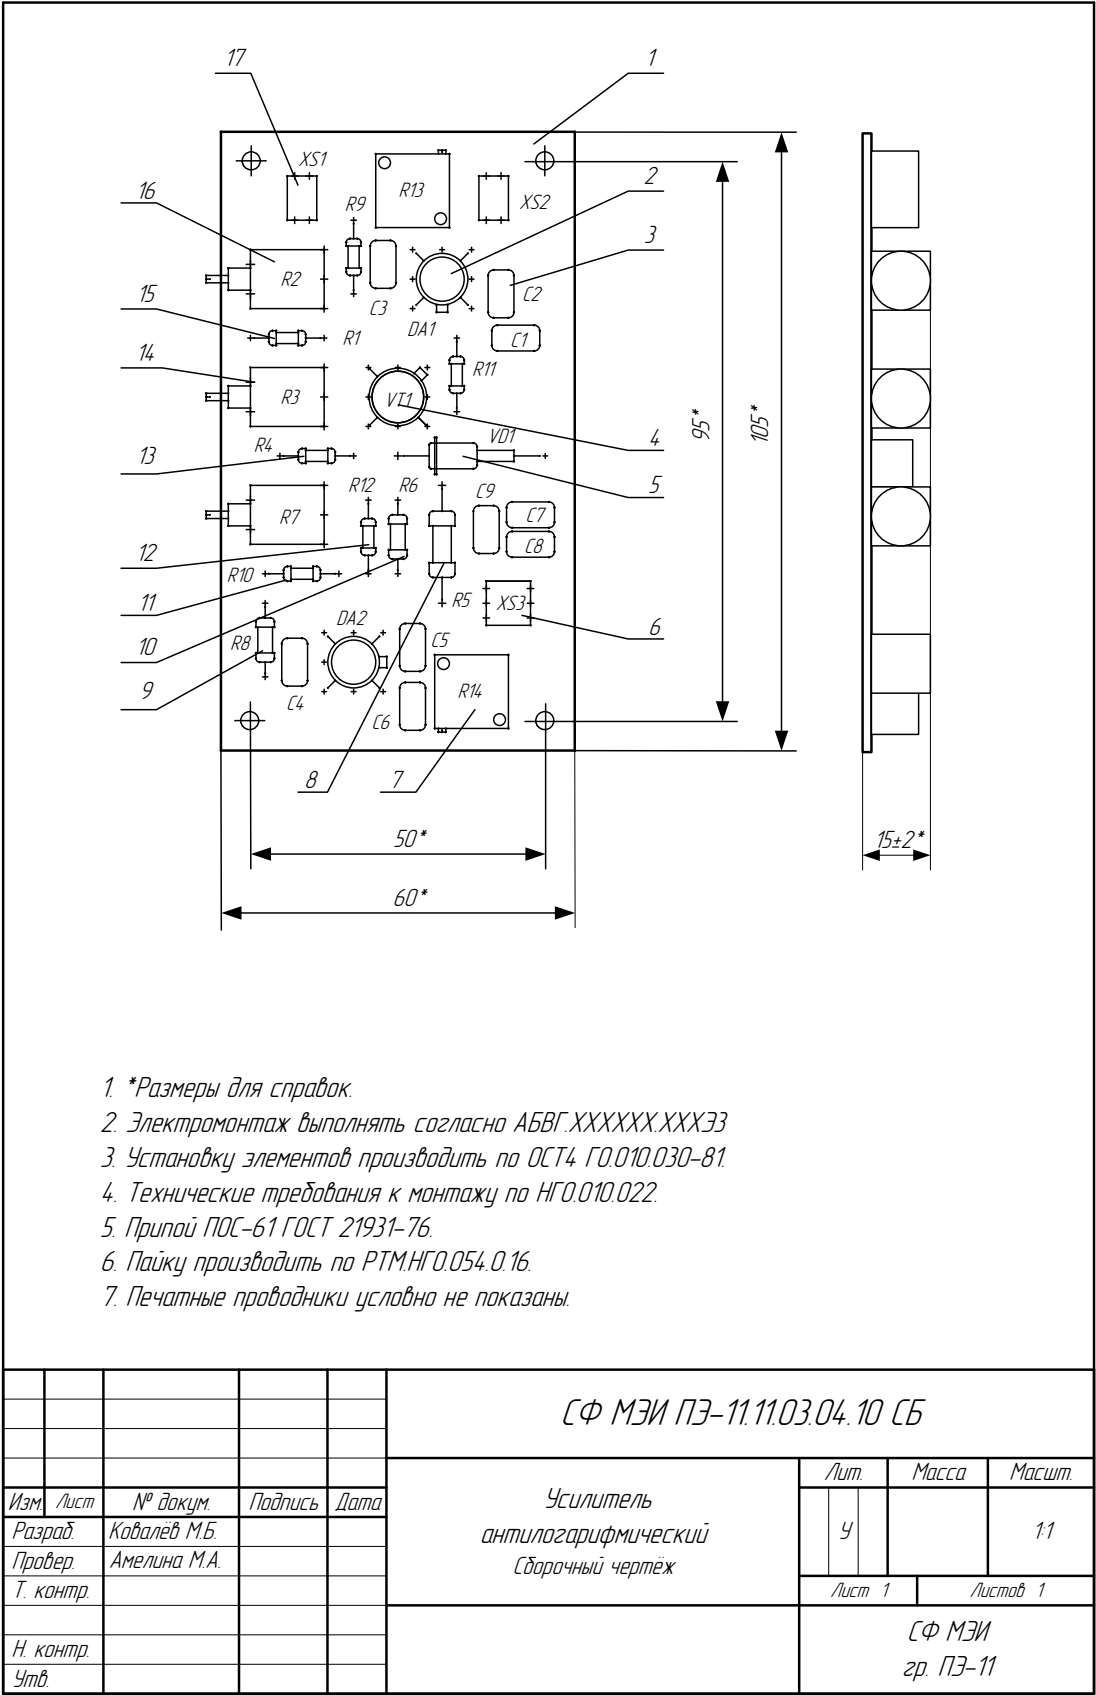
Пример выполнения сборочного чертежа
